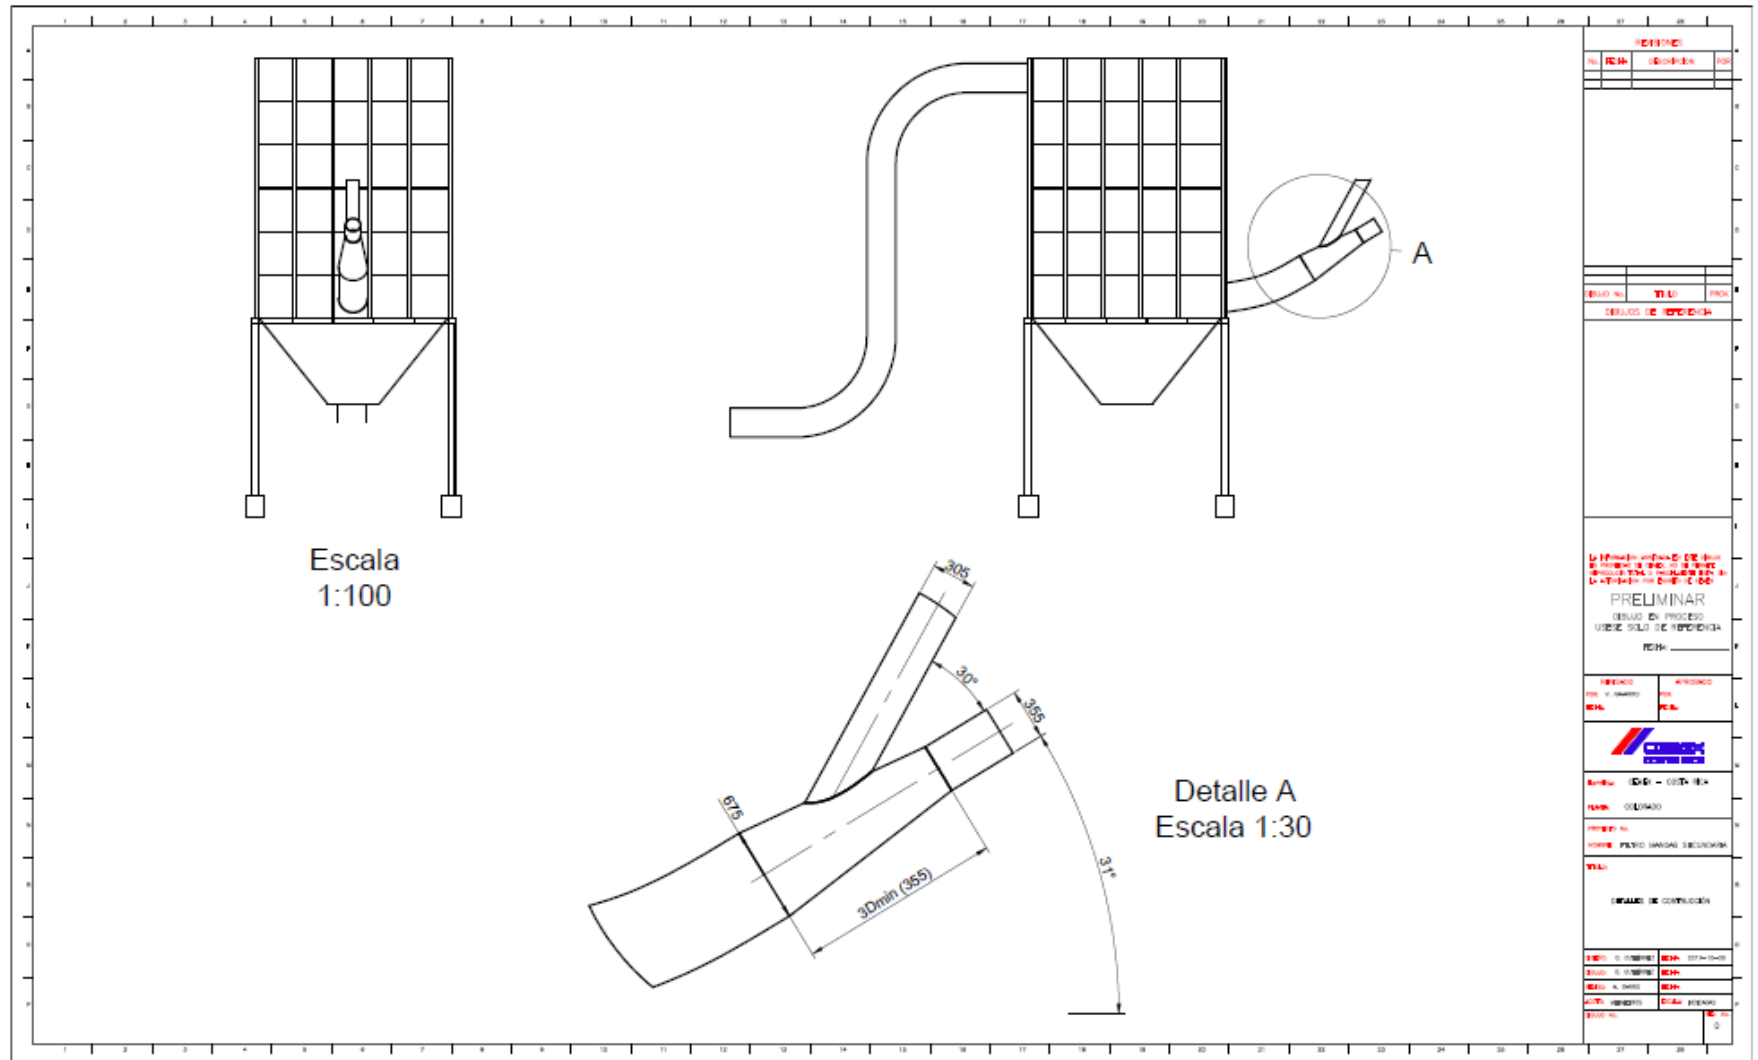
Detalles de conexión de tuberías ideal sin prevista a la entrada del filtro.
